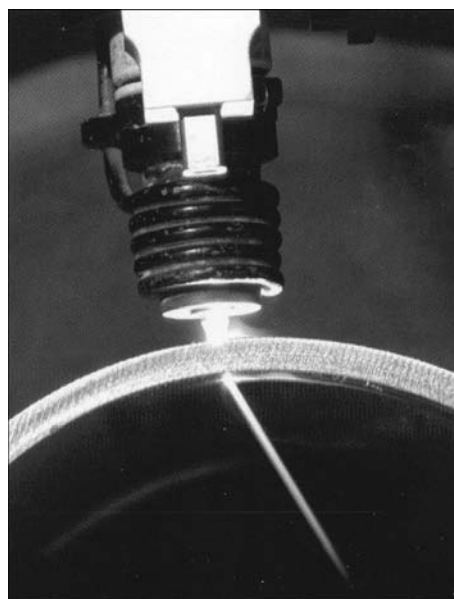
К-ТИГ сварка поворотного стыка трубы толщиной 13 мм
